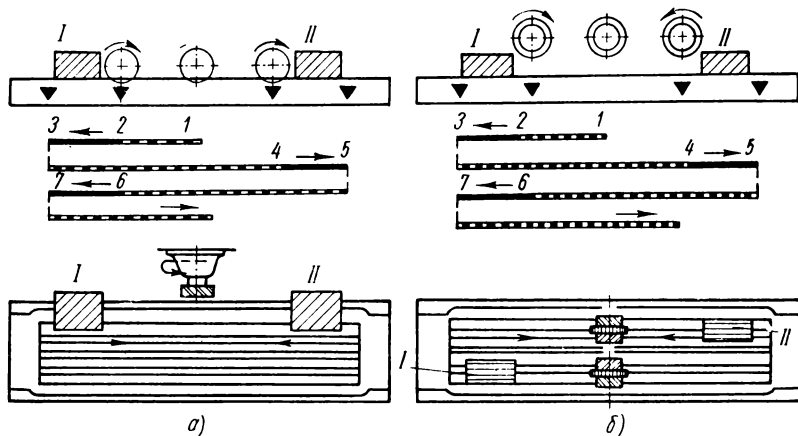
Схемы фрезерования с использованием обратного хода стола:
